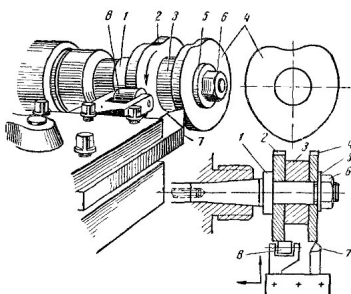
Обтачивание профиля дискового кулачка по копиру
